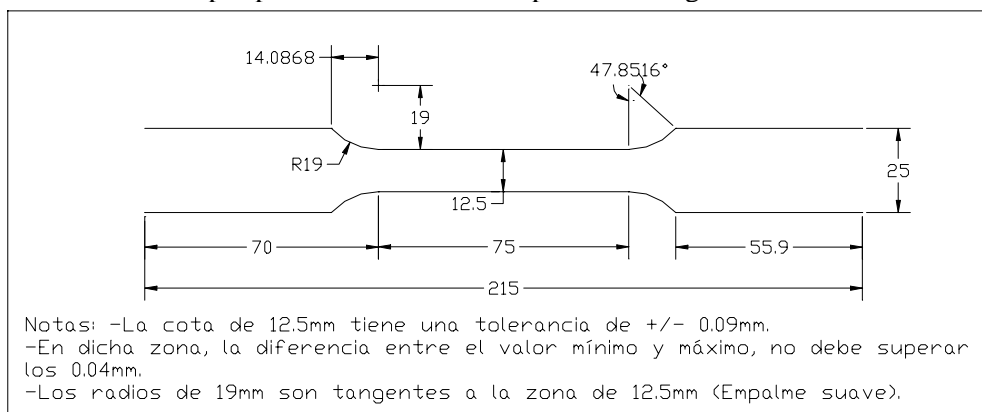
Plano de fabricación de probeta plana de tracción normalizada.
